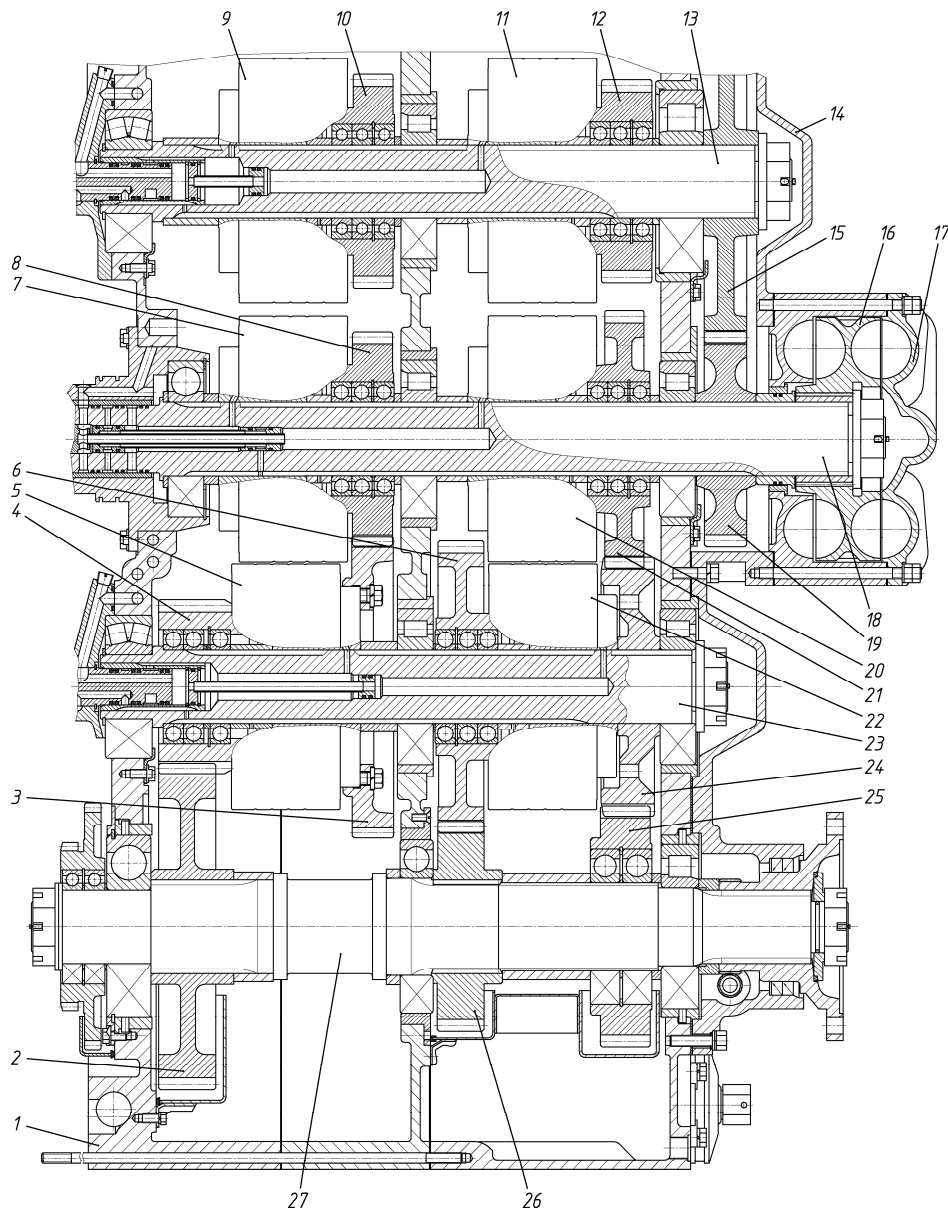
Коробка передач карьерного самосвала БелАЗ-7555Е
